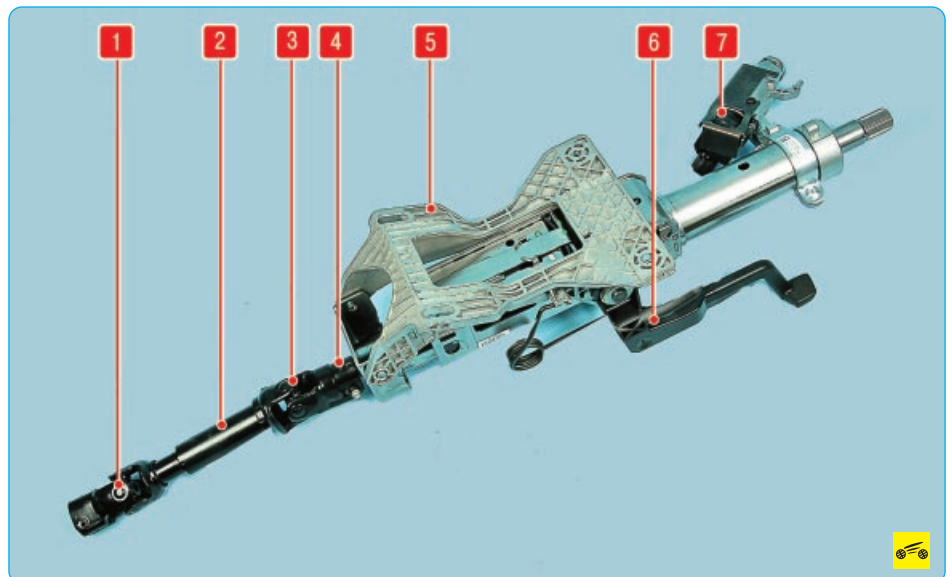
Рулевая колонка: 1, 3 – карданные шарниры промежуточного вала; 2 – промежуточный вал; 4 – вал рулевой колонки; 5 – корпус рулевой колонки; 6 – механизм регулировки положения рулевой колонки; 7 – выключатель (замок) зажигания
